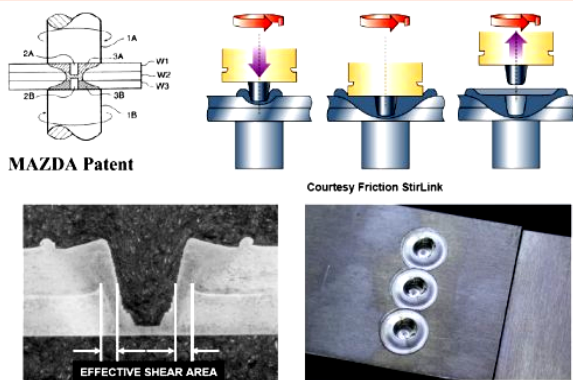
Soldadura de Fricção por Pontos Spot Friction Welding, variante da SFW-Stir Friction Welding (SFL). [68]
